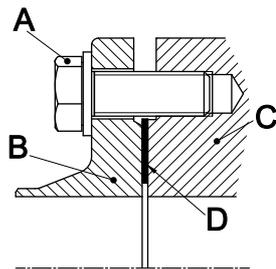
Anschluss Hauptleitung auf Pumpengehäuse.
